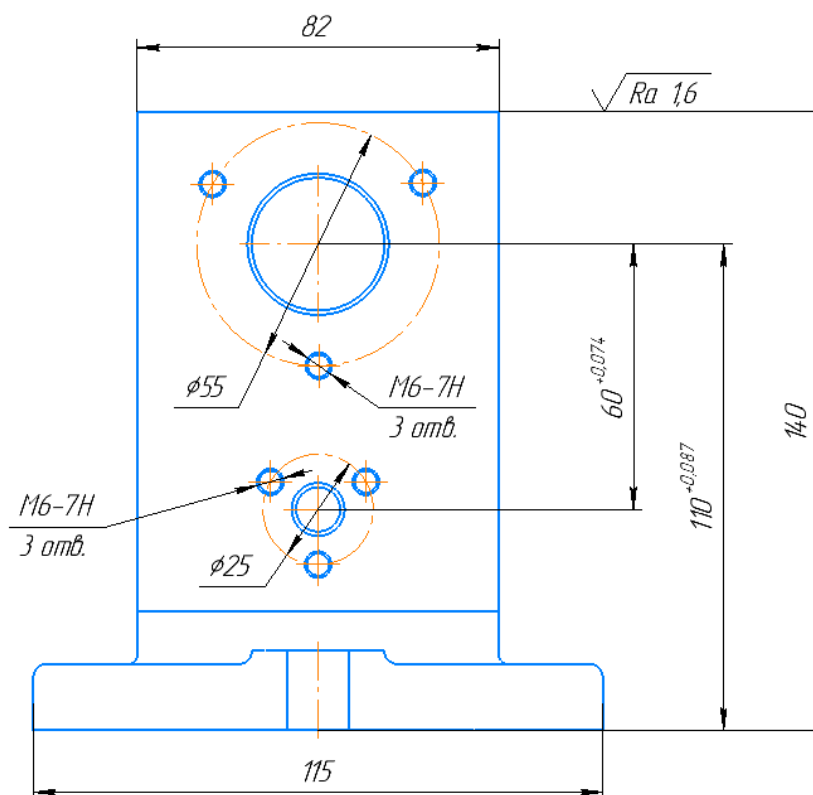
Чертеж детали 2 до метрологической экспертизы (вид сбоку)
